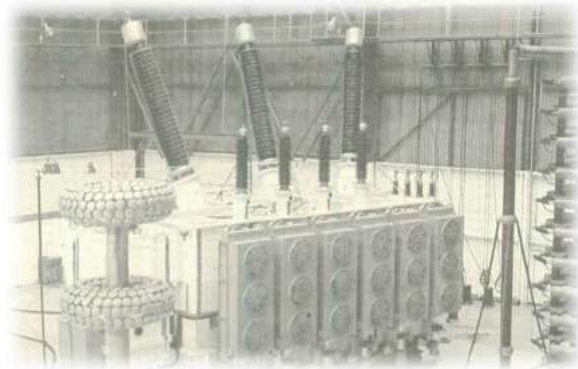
Criterio de diseño y montaje de accesorios finales de Transformador Acorazado en Plataforma de Ensayos propiedad de CENEMESA.
